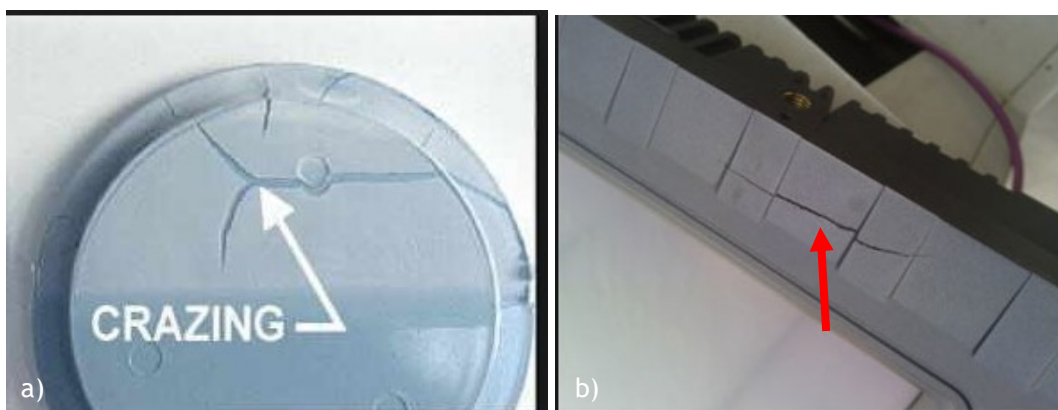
a) e b) zonas de aparecimento de fissuras. [37]
